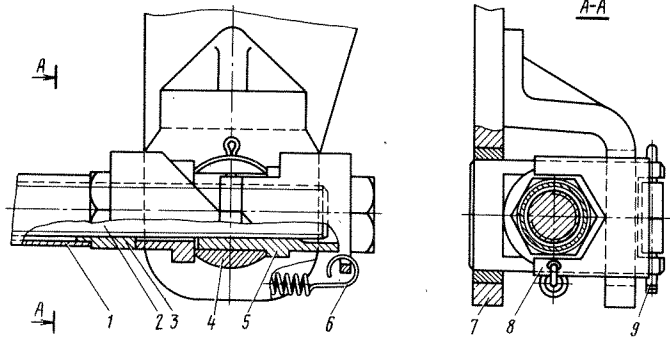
Регулятор выхода штока тормозного цилиндра:
